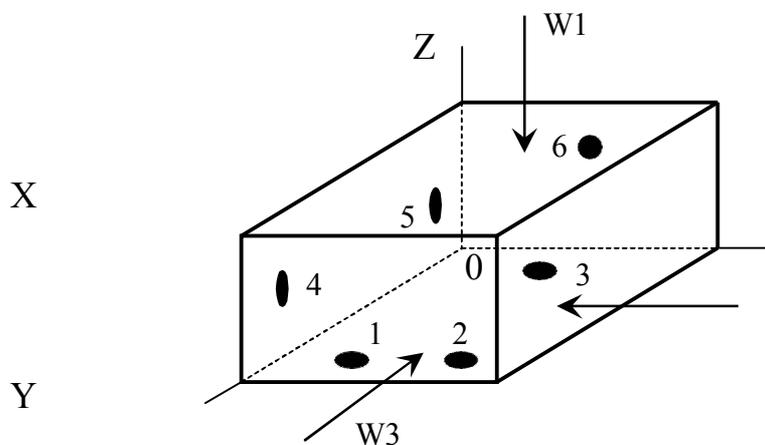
Схема базирования и зажима заготовки в приспособлении
